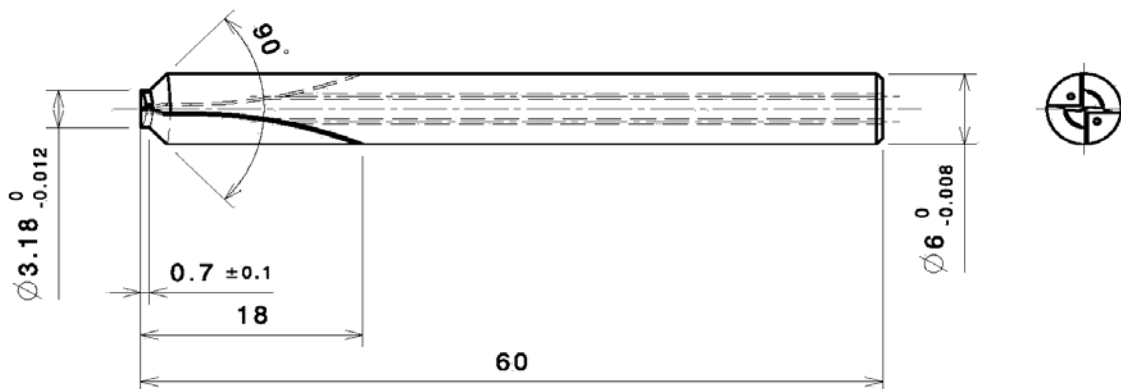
Чертеж твердосплавного сверла VOF D3.18X0.7X 60-6 из сплава UF10
